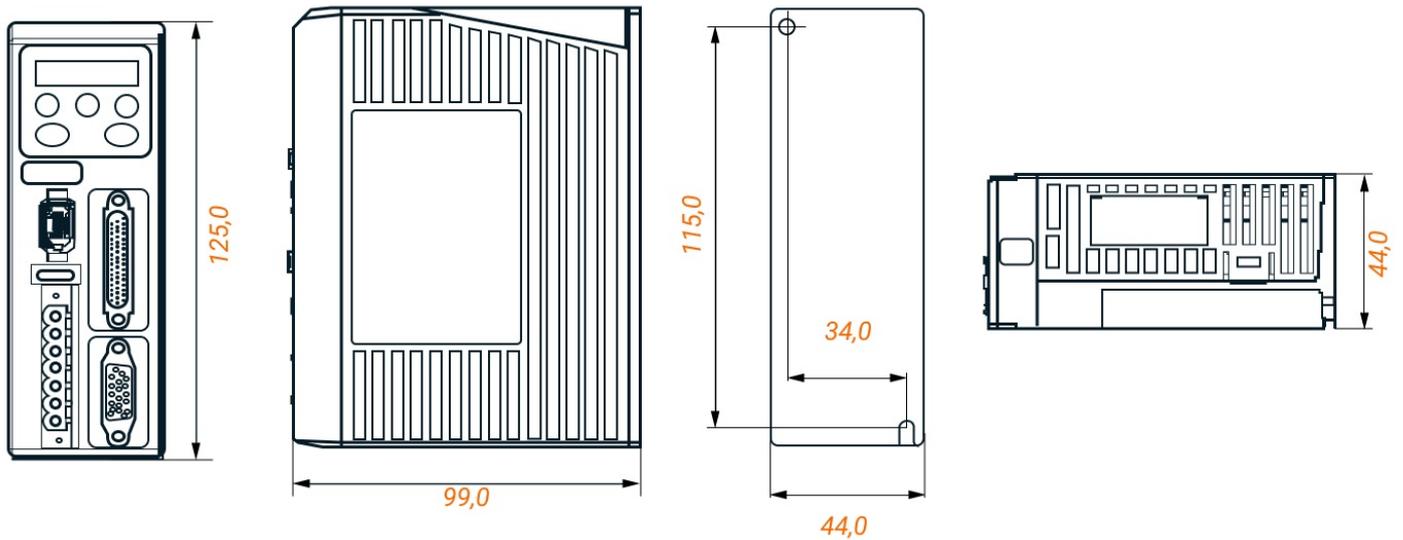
Габаритные размеры серводрайвера ELD5-400
